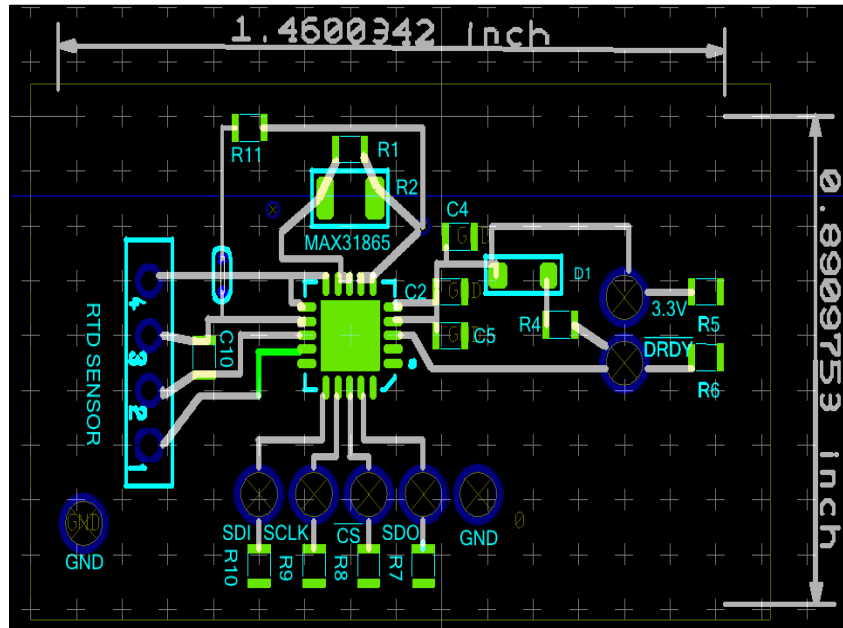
Diseño de placa del PCB que no incluye la parte que convierte USB a PIN Master.
